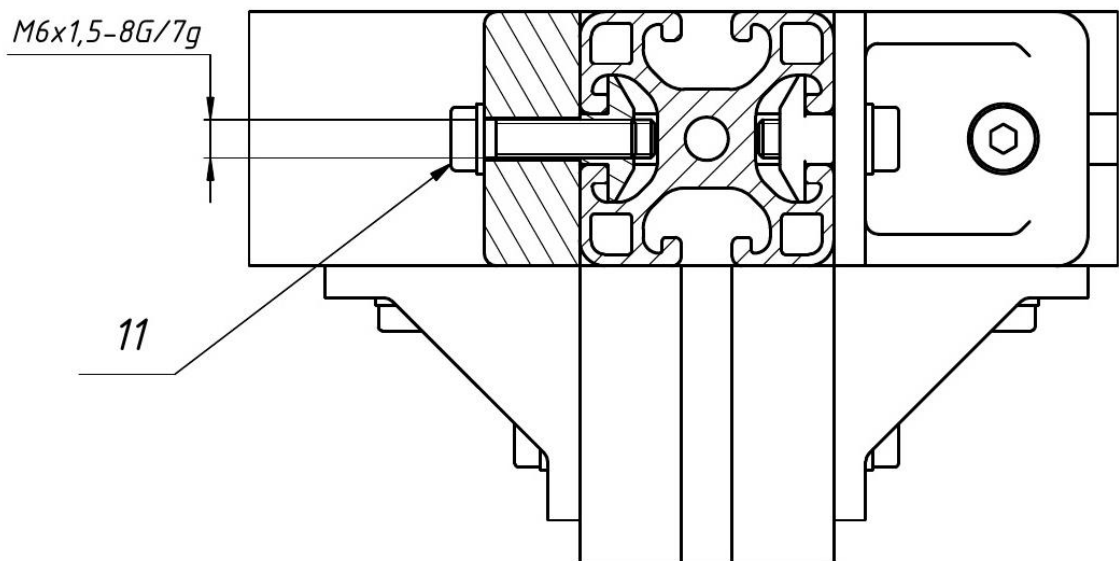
Станина несучої системи гравіювального верстату
